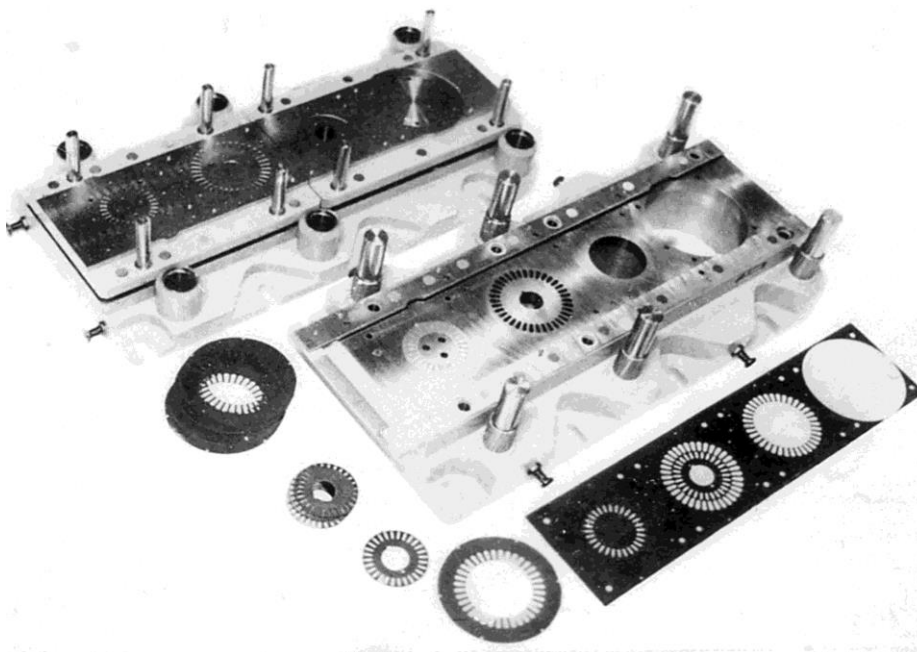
Элементы штампа для изготовления пластин статора и ротора
